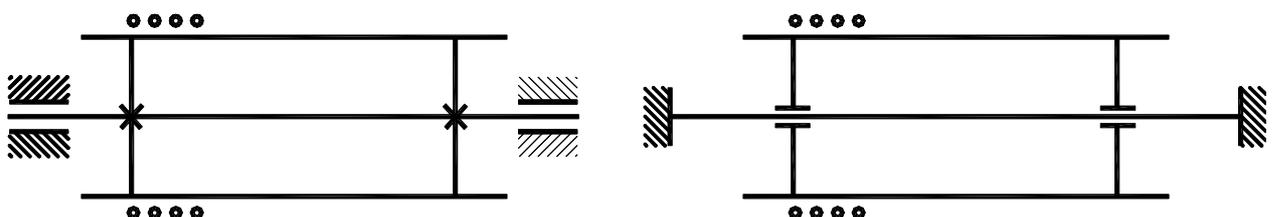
Схемы барабана с вращающейся и неподвижной осью
